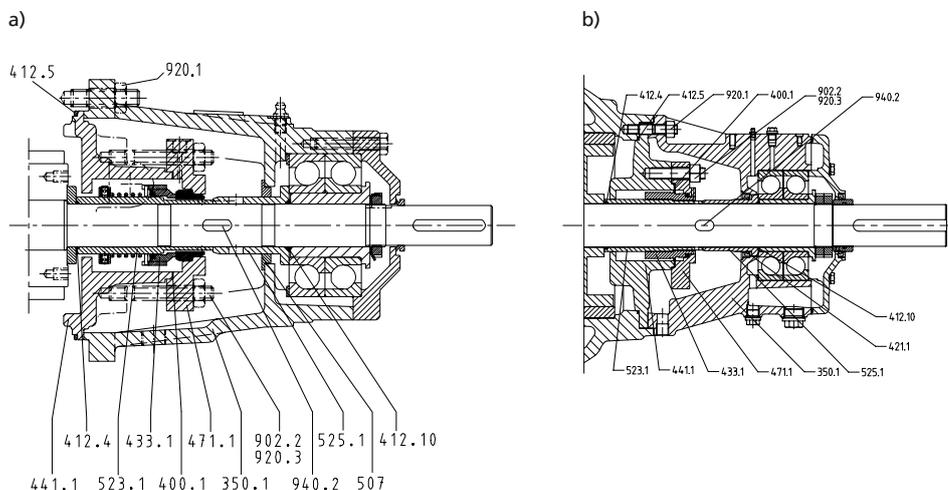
Демонтаж торцевого уплотнения: а) типоразмеры 32-200 и б) типоразмер 250
